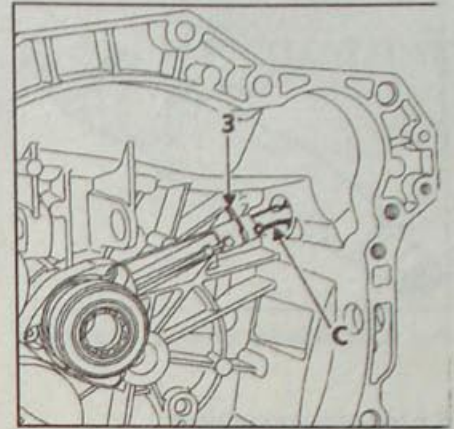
Расположение фиксатора (3) крепления штуцера (С) рабочего цилиндра сцепления
